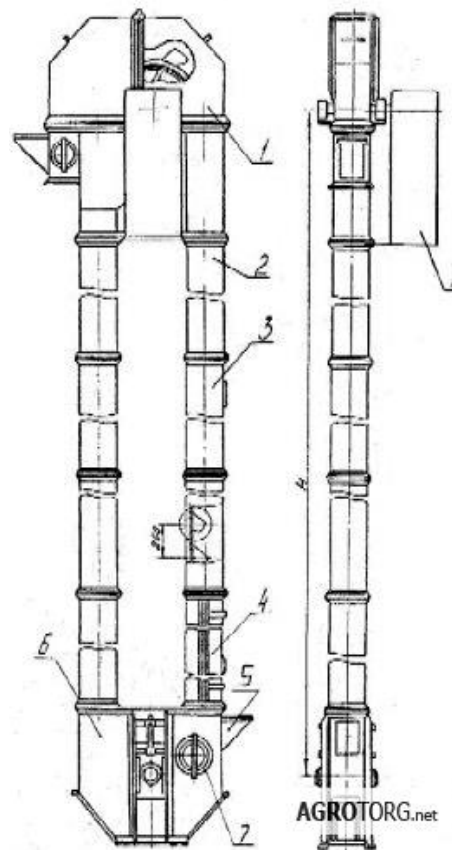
Загальний вигляд норії стрічкової ковшового:
